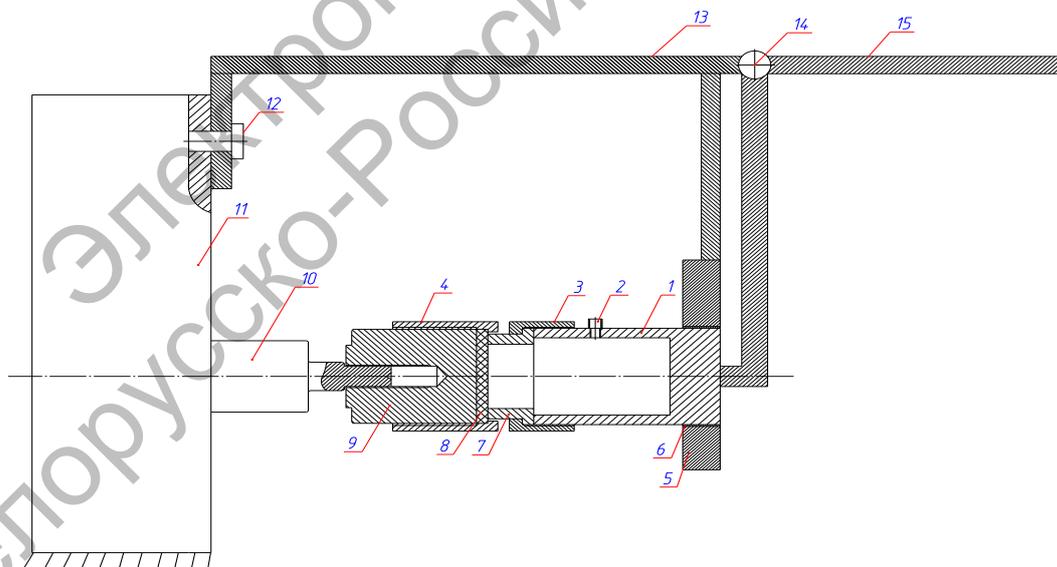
Схема приспособления для триботехнических испытаний резин методом торцевого трения: 1 – стакан, 2 – штуцер, 3 – крышка стакана, 4 – крышка цилиндра, 5, 13 – детали корпуса, 6 – бронзовая втулка, 7 – сменное кольцо, 8 – резиновое уплотнение, 9 – цилиндр, 10 – вал, 11 – машина трения СМТ – 1, 12 – болт крепежа, 14 – шарнир, 15 – рычаг нагружения
